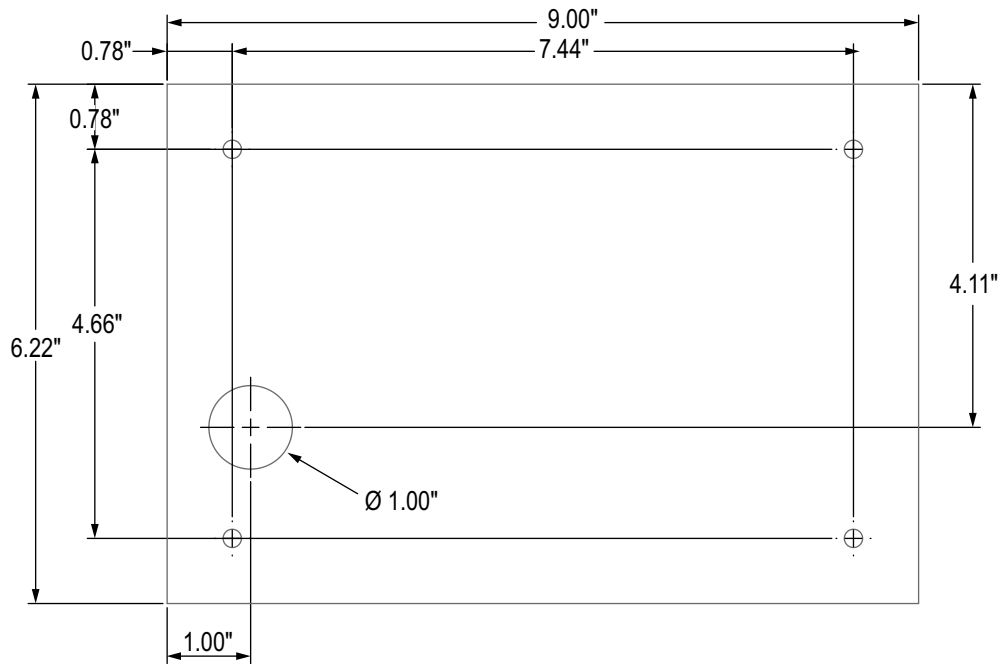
Dimensions du support à panneau pour modèle tactile 7 pouces
